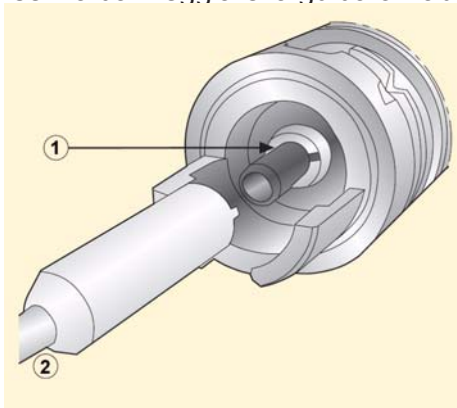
2: Montaggio corretto del tubo di trasmissione
